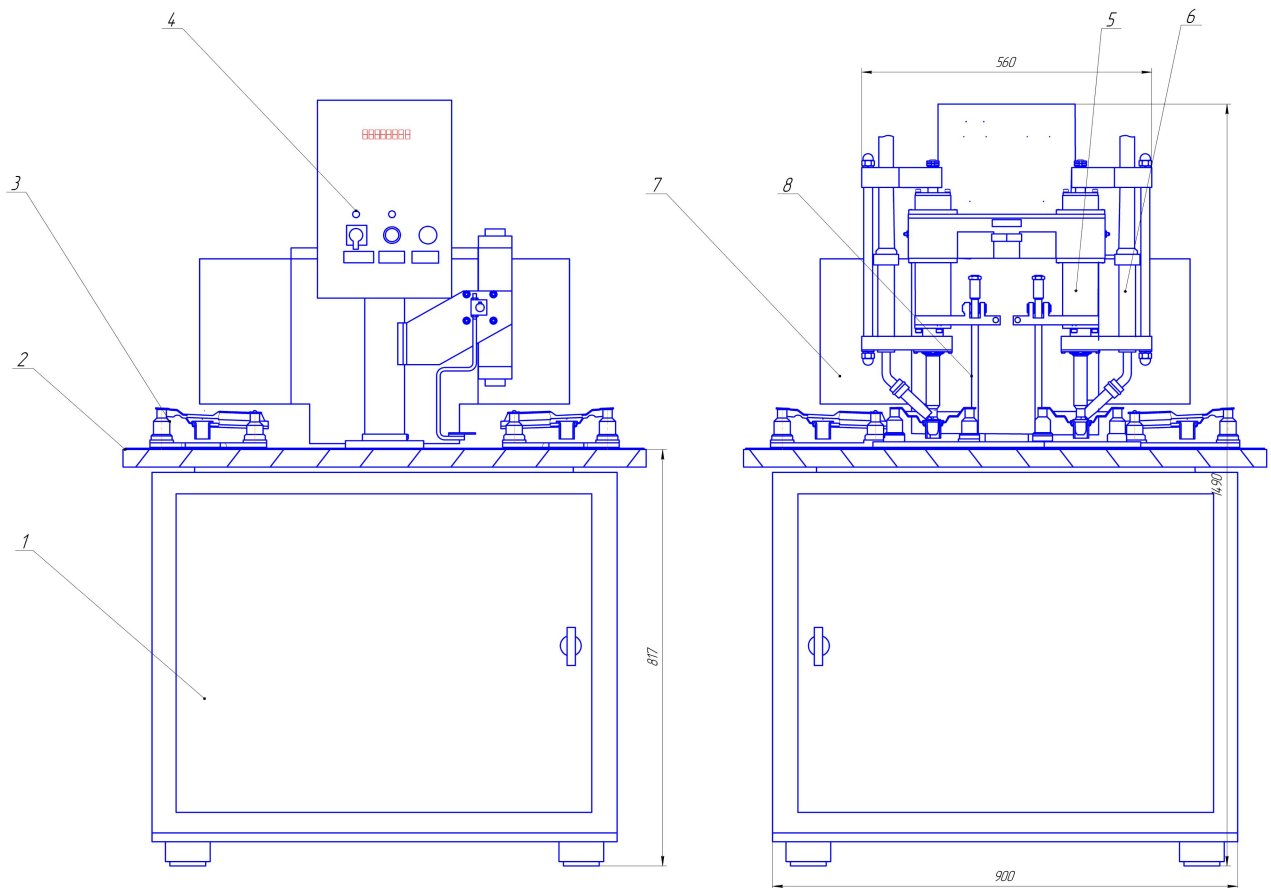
Загальний вигляд зварювальної установки:
